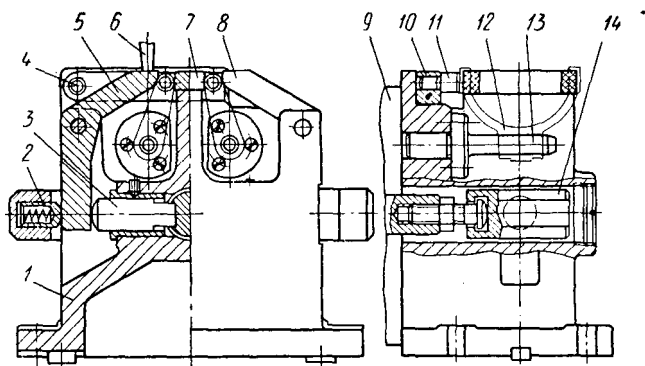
Двухместное фрезерное приспособление для обработки наружных поверхностей вилок
